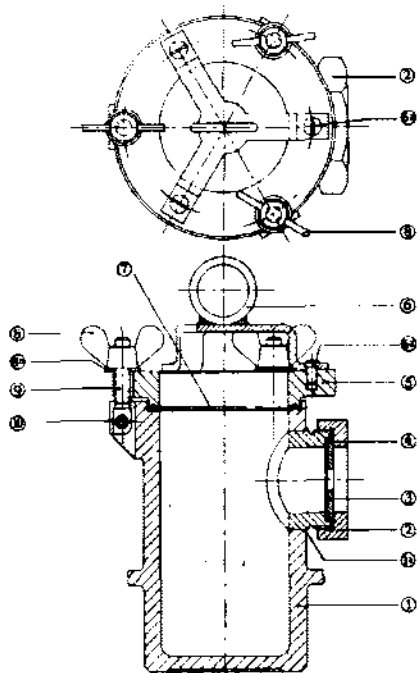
Recipiente a presión, montado vistas esquemáticas en corte vertical y en planta dimensiones en mm
